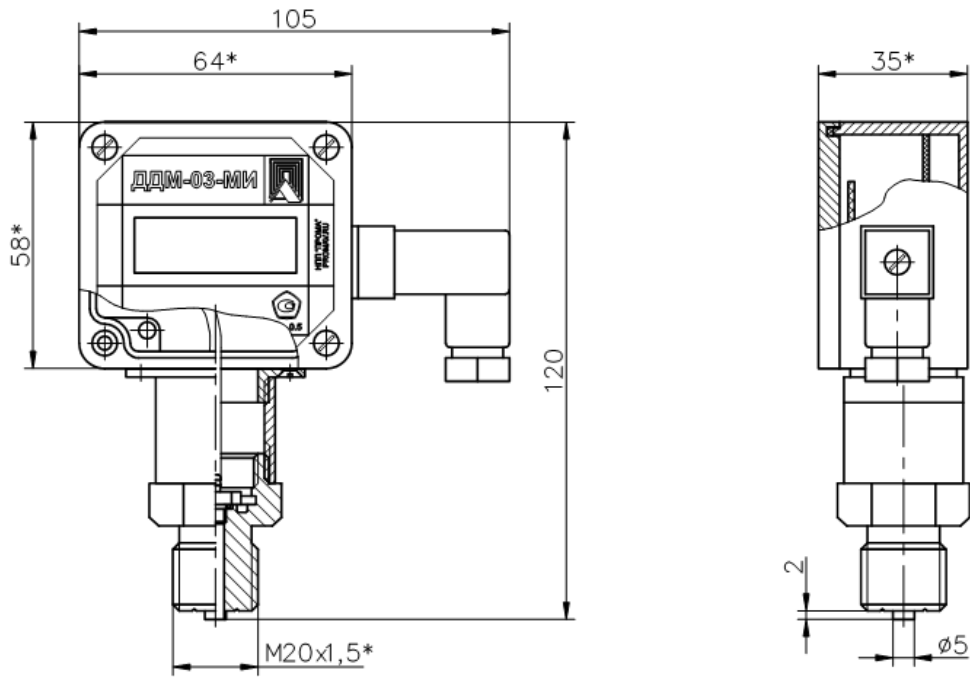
б. Габаритные и присоединительные размеры датчика ДДМ-03-ДИ(ДВ,ДИВ,ДА)-МИ с индикатором. Конструктивное исполнение по штуцеру 2.
